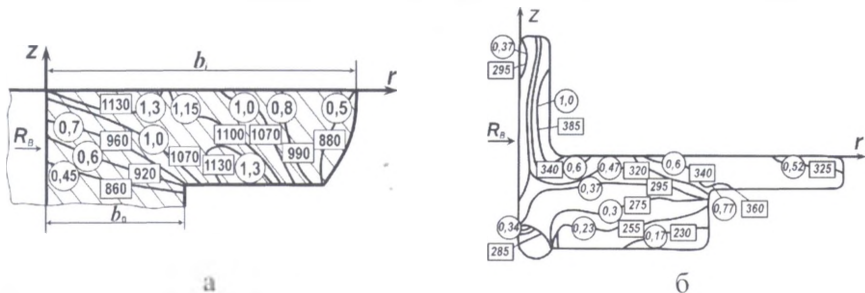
Характер розподілу в перерізі зовнішнього бурта трубної заготовки (а) і кільцевої заготовки (б), параметрів $e_u = const$, $\sigma_u = const$ за результатами вимірювання твердості
